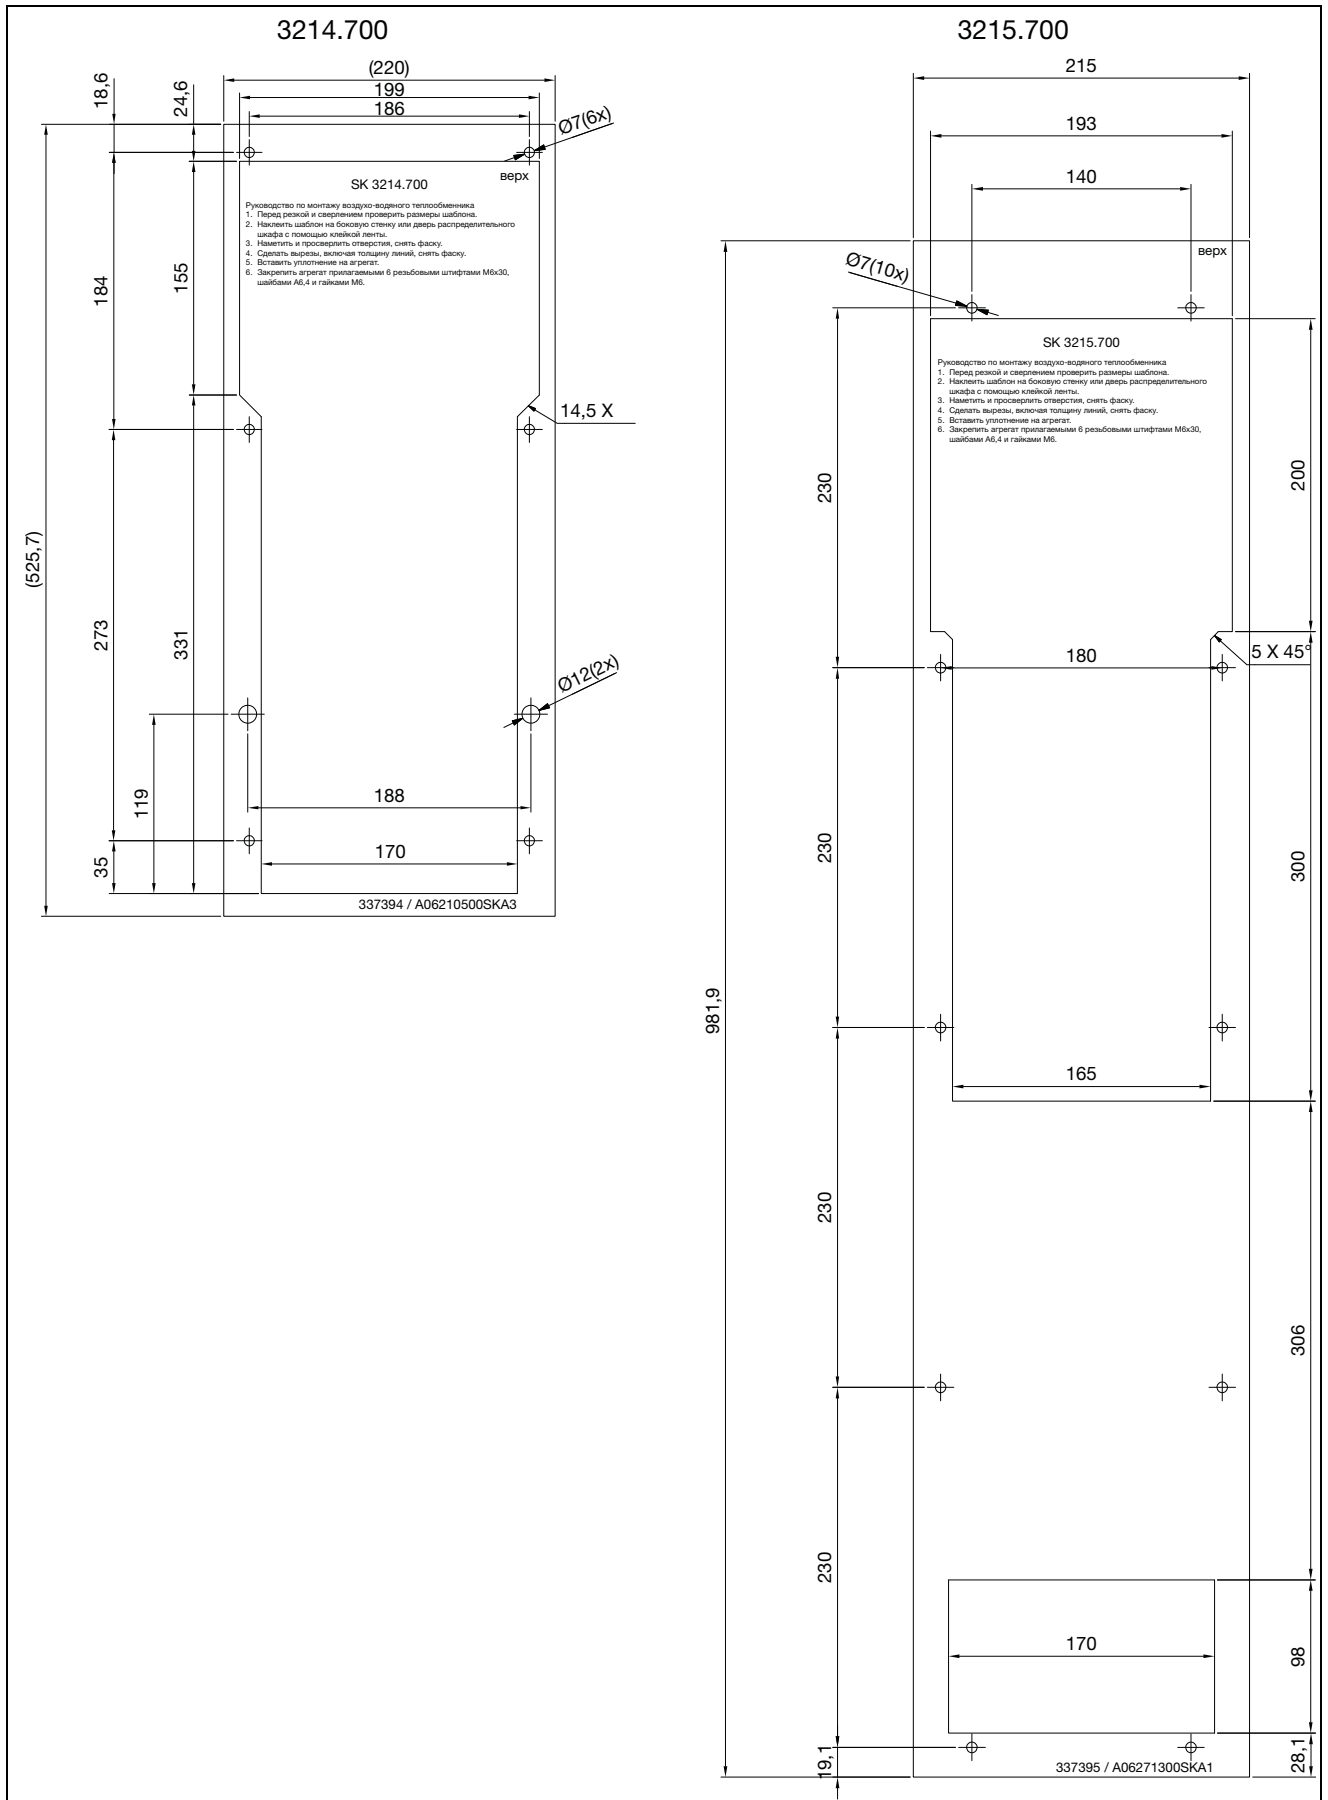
Размеры вырезов и отверстий 3214.700 и 3215.700
